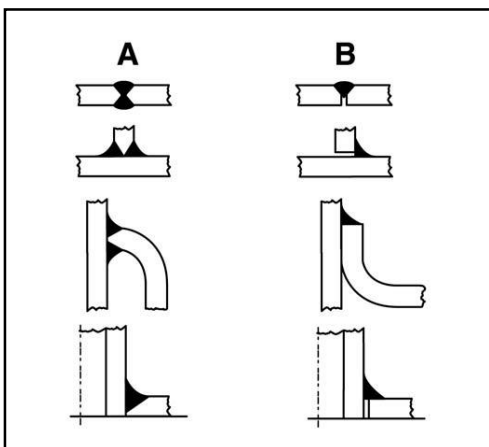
Ausführungsbeispiele Schweißverbindungen
